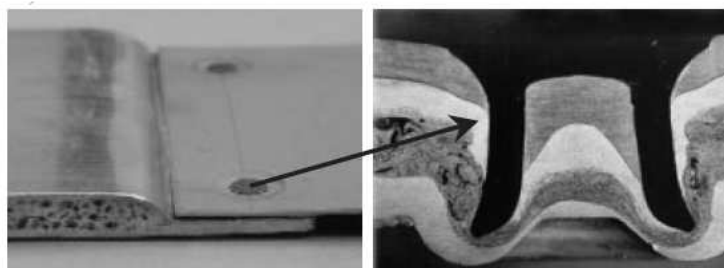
38 Metodi di giunzione meccanica: punzone di rivettatura [See02]
